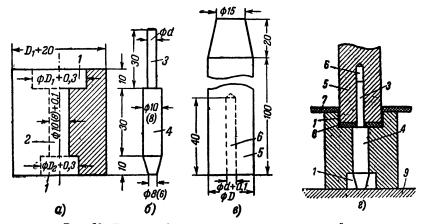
Приспособление для пробивки отверстий. а — двойная матрица; б — ловитель - выталкиватель; в — пуансон, г — взаимодействие частей.
